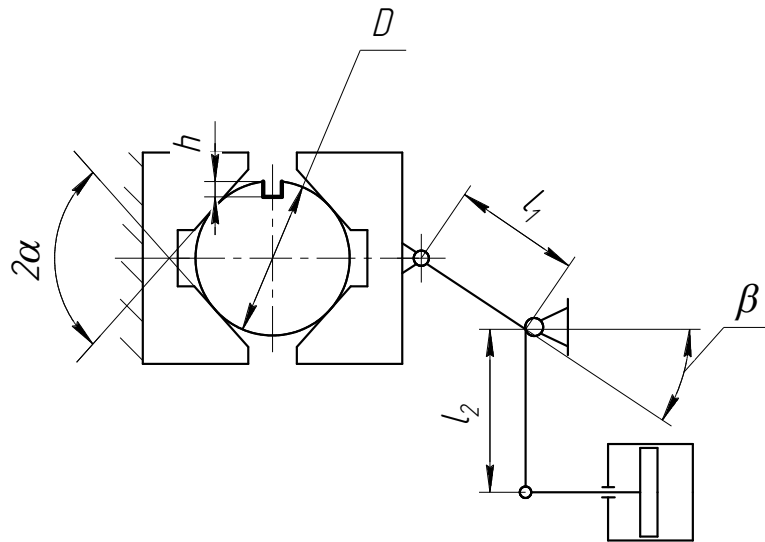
Принципова схема механізованого пристосування для фрезерування шпонкового пазу кінцевою фрезою
